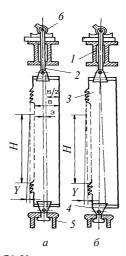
Установка пил в захватах: a — пильная рамка установлена с уклонам, соответствующим величине посылки; δ — пильная рамка установлена без уклона; l — верхняя поперечина пильной рамки; 2 — захват верхний; 3 — пила; 4 — захват нижний; 5 — нижняя поперечина пильной рамки; 6 — эксцентриковый захват
